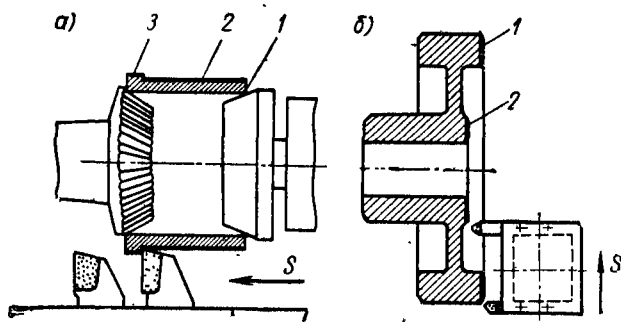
Примеры одновременной обработки двух поверхностей двухрезцовыми державками.
